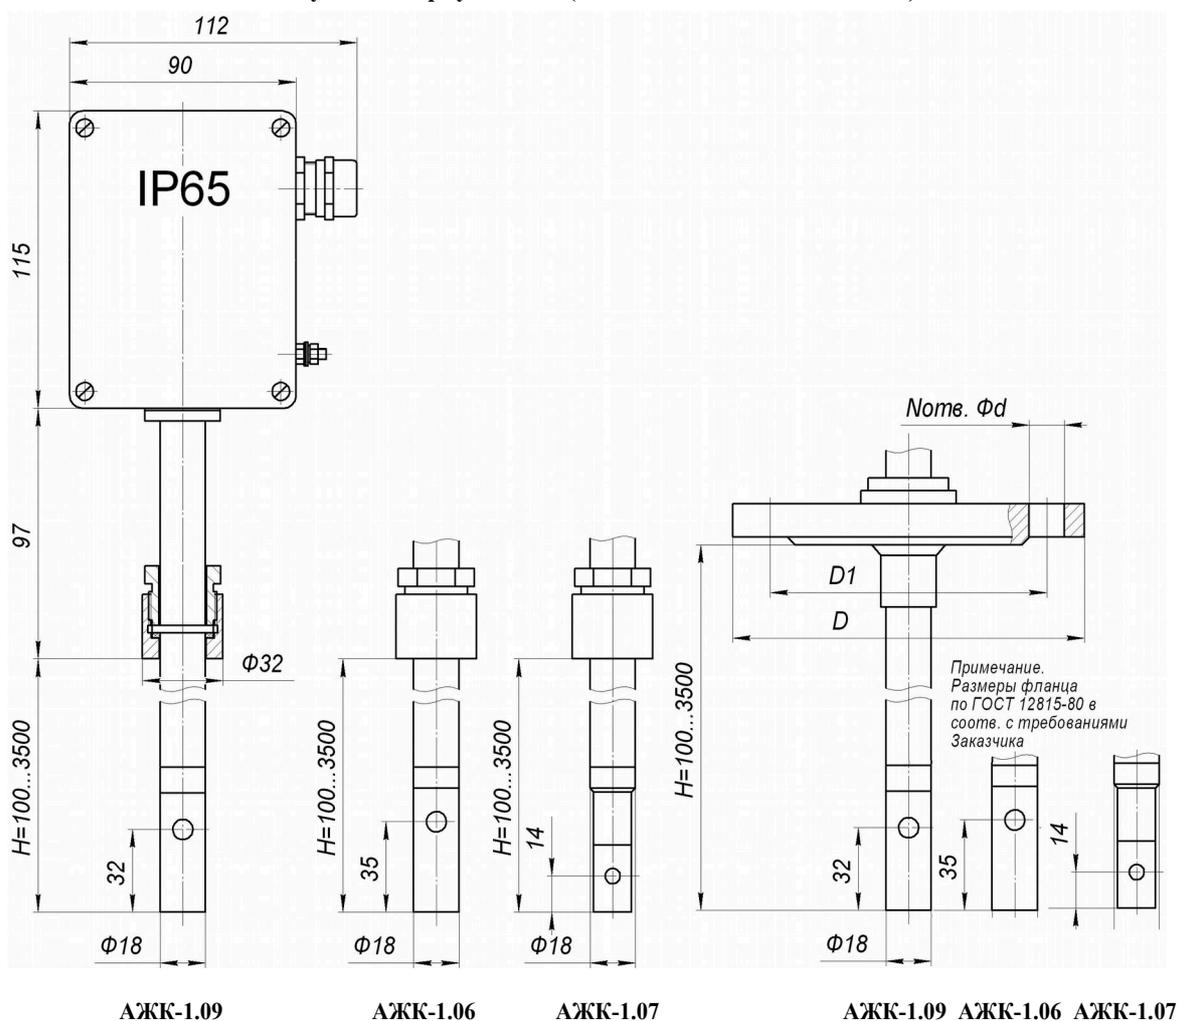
Габаритные и монтажные размеры проточных датчиков (показано с корпусом электронного блока «Д», но может быть с корпусами «Н» и «И») - с бобышкой / с фланцем
